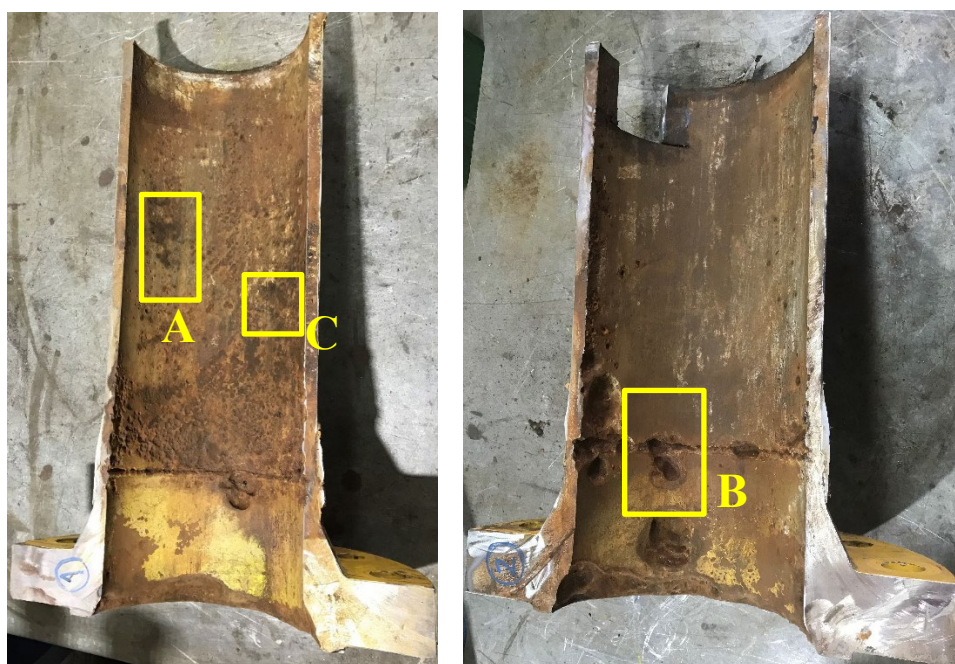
Vista interna. Pits de corrosión sobre el lado caño, y ataque tipo zanja sobre soldadura. A) y B) defectos de mayor tamaño y ataque preferencial sobre soldadura (detalle en 5). C) Defecto pasante (detalle en 6).
